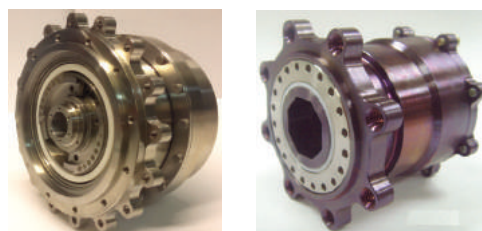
Прецизионная волновая зубчатая передача (а); планетарный зубчатый редуктор механизма раскрытия (б) с  $M_{ном} = 8$  кгс·м
